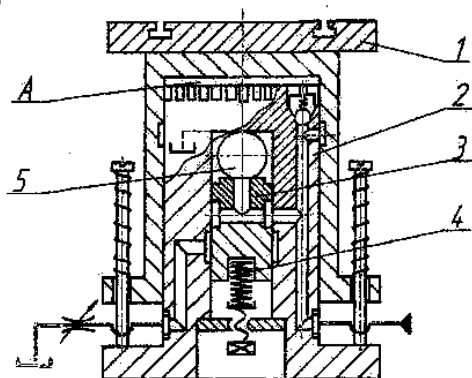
Схема малогабаритного гідравлічного віброзбуджувача з зворотним зв'язком по тиску золотникового типу (ударний): 1 - стіл робочий; 2 - плунжер; 3 - золотник; 4 - пружина; 5 - кулька
